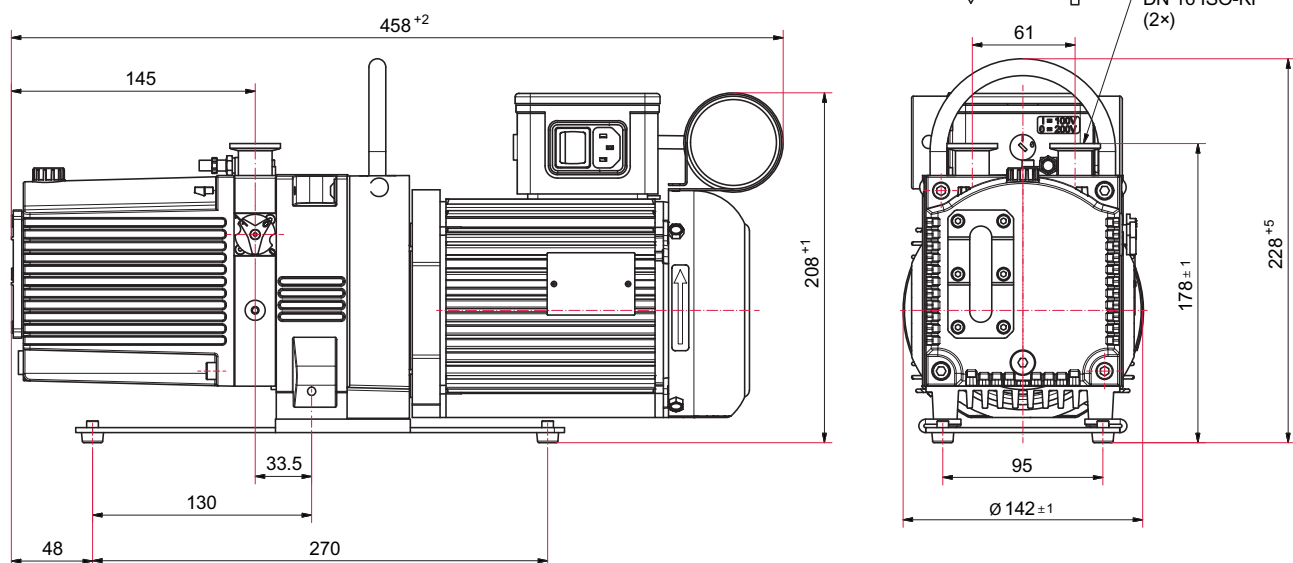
Dimensões do Duo 6 M, motor monofásico, 100/200 V, 50/60 Hz
